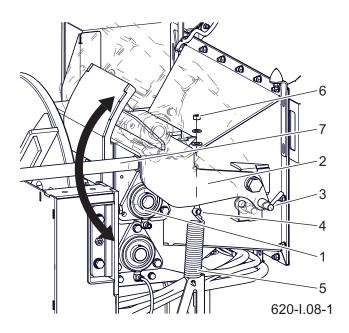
Rodillo superior, levantado (1) rodillo superior (2) brazo de rodillo (3) protección (4) perno de resorte (5) resorte (6) tuerca (7) palanca del rodillo
